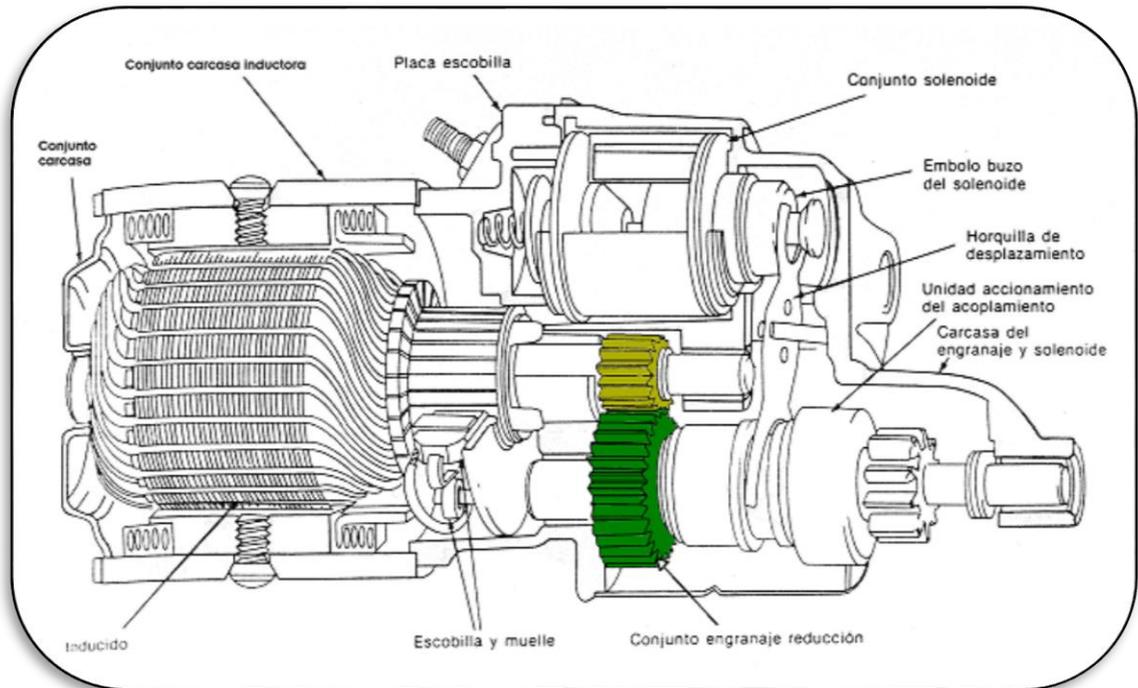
Motor de arranque con engranaje de reducción y acoplamiento de rueda libre.
